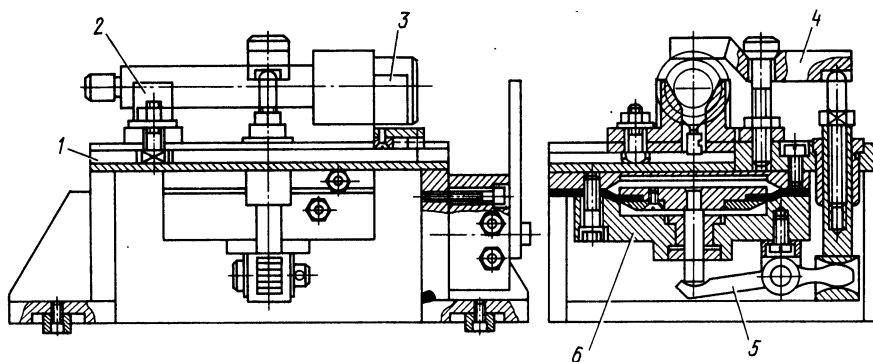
Универсальное приспособление для фрезерования шпоночных пазов и лысок на валиках
